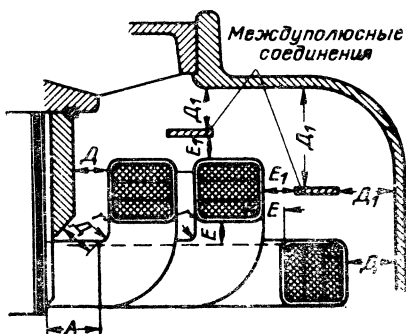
Расположение лобовых частей однослойной обмотки.
